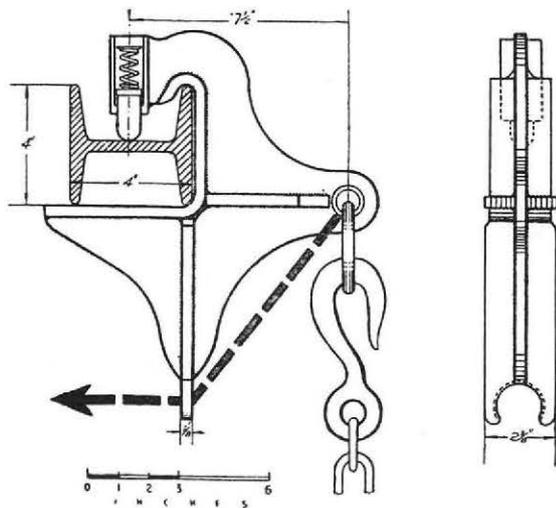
Dispositif de torsion pour étançon en poutrelle d'acier de 100 × 100 mm.
